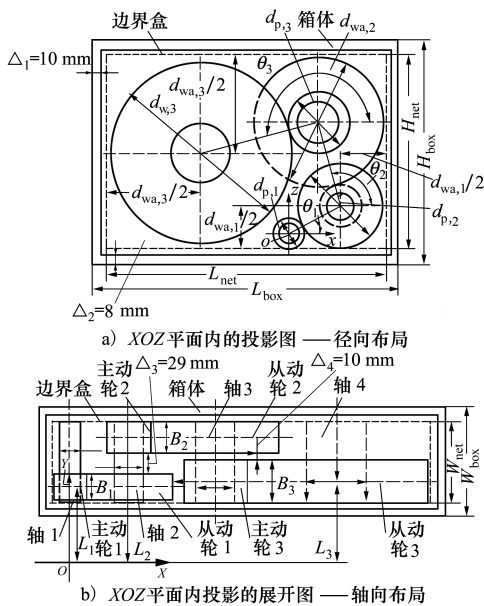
ZSY 型 3 级圆柱齿轮减速器最优解的布局形式
